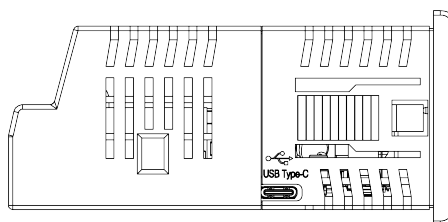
Расположение разъема USB для корпуса Щ2
